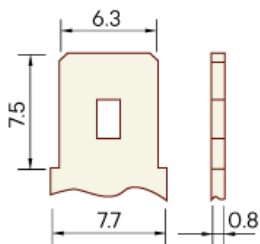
Внешний вид и габаритные размеры выводов подключения внутренних АБ
